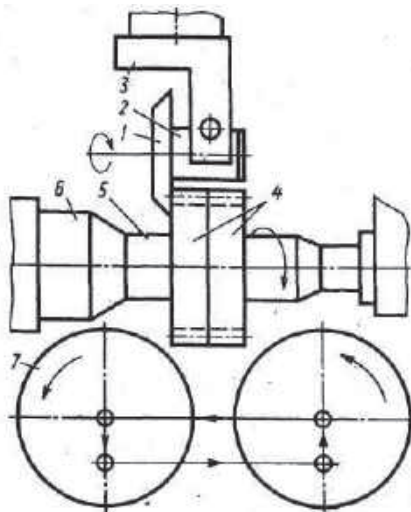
Устройство для снятия заусенцев с зубьев зубчатых колес, обрабатываемых на зубофрезерном станке
